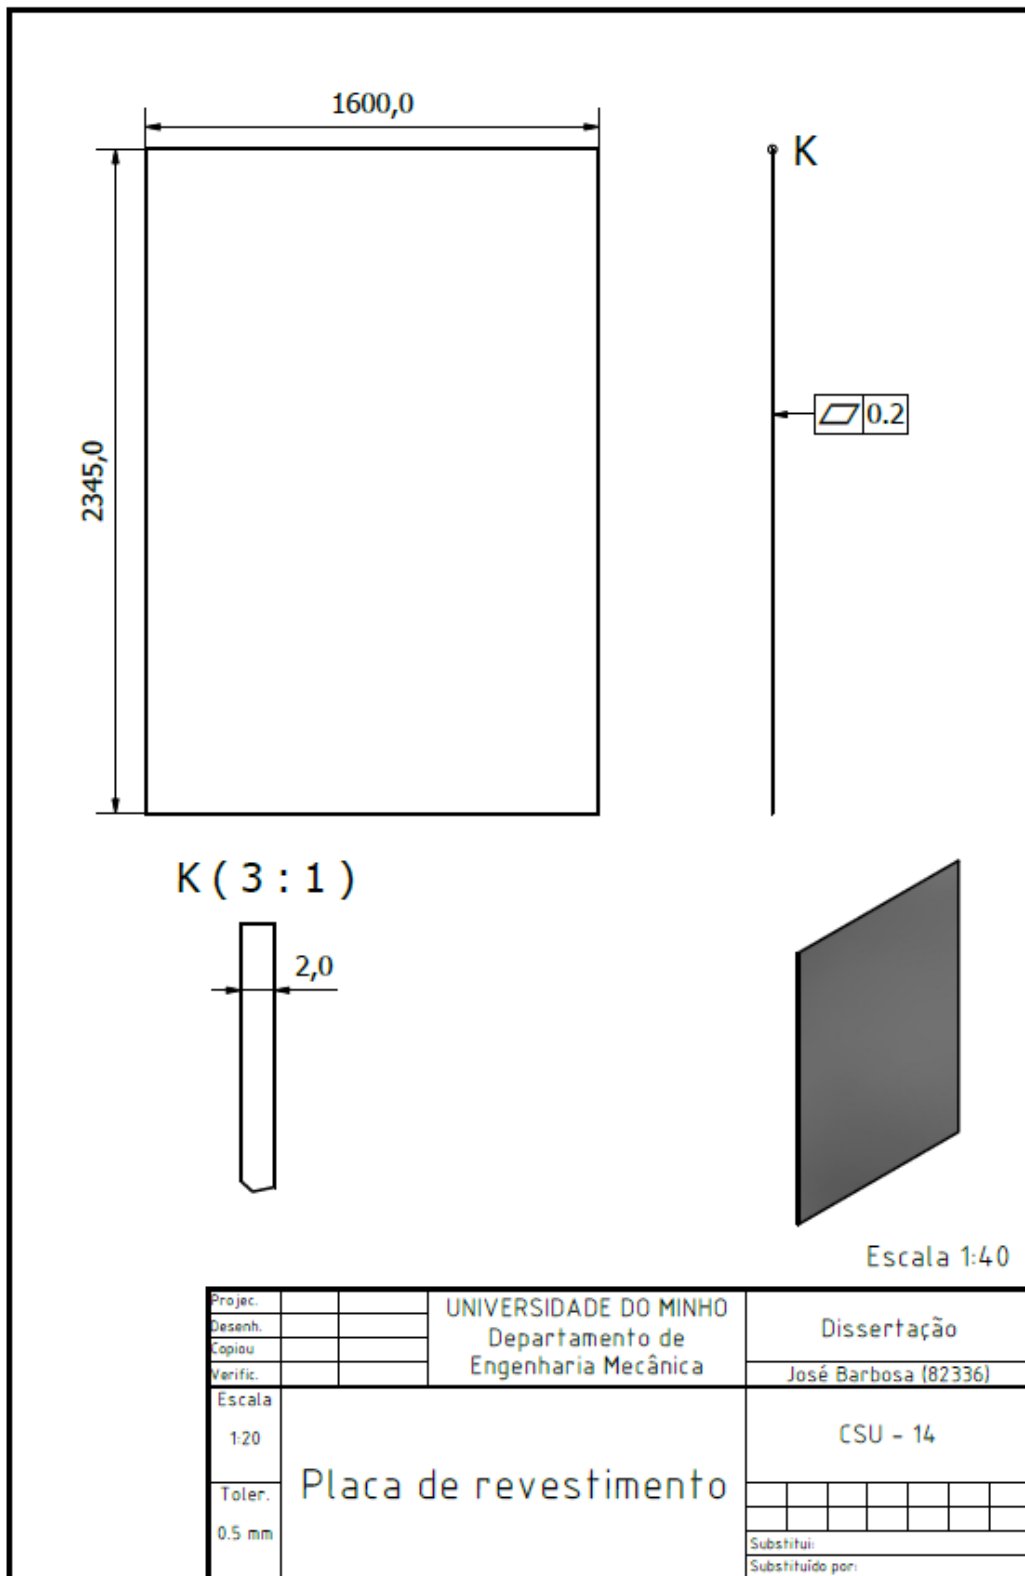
Figura Anexo III-17 – Desenho técnico da placa de revestimento.
